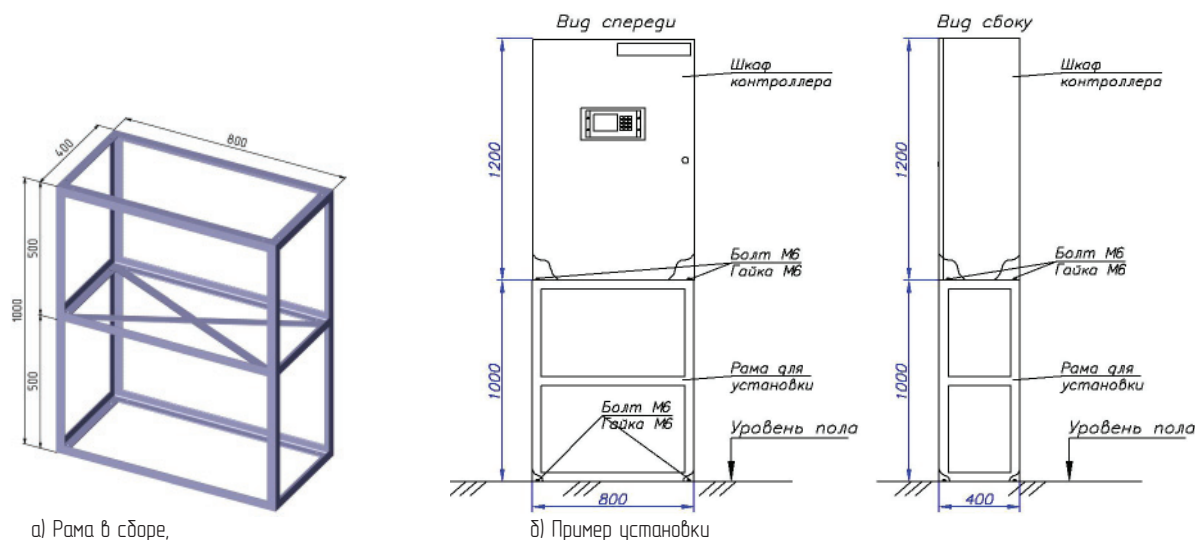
Установка шкафа 1200*800*400 мм на горизонтальную поверхность в помещении
